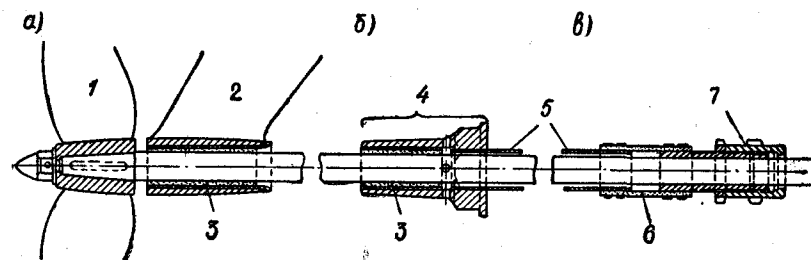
Детали эластичного крепления вала: а — резиновый подшипник в двуплечем кронштейне гребного вала; б — резиновый подшипник в кормовом конце дейдвудной трубы; в — амортизированная опора — сальник с резиновой муфтой, позволяющий ей совершать колебания вместе с двигателем и валом.
